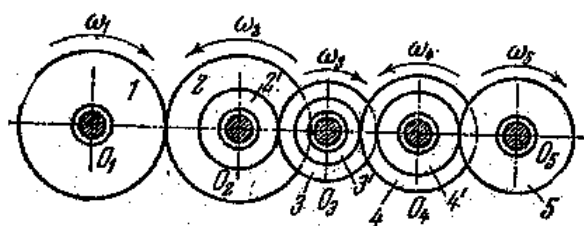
Рядовое соединение зубчатых колес:
